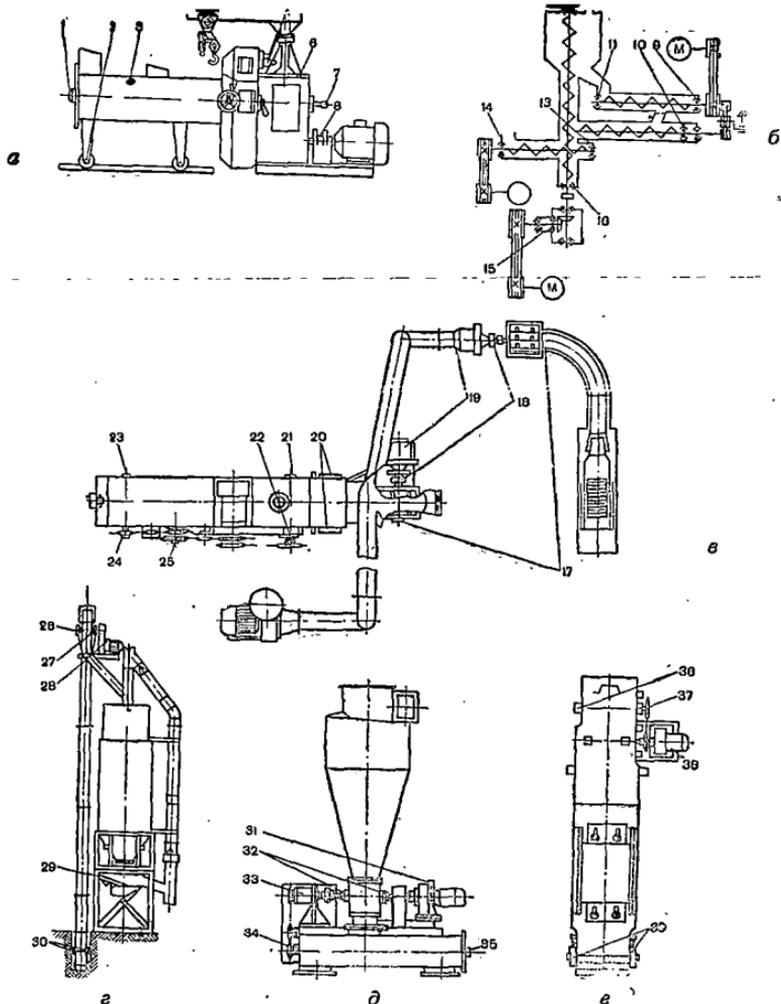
Схема смазки оборудования для прессования кормов ОПК-2:
